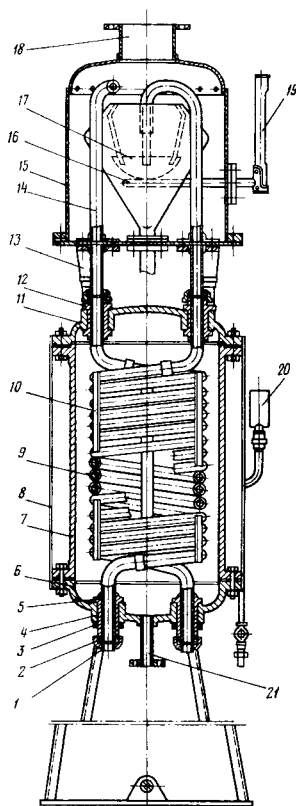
Двухзмеевиковая помадоварочная колонка
